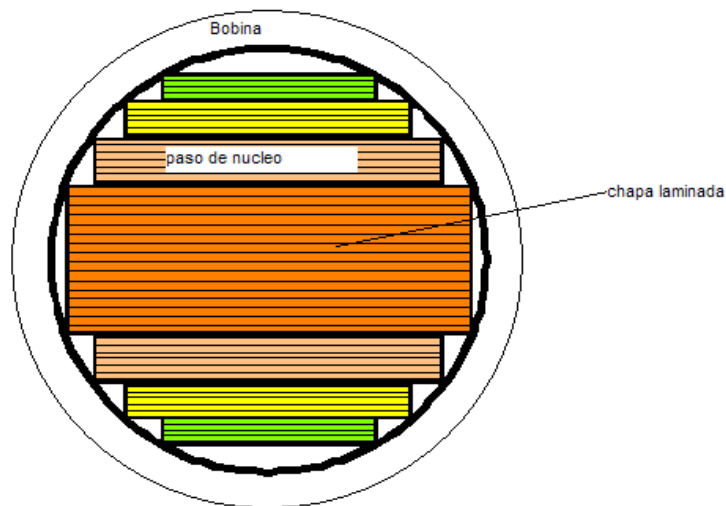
Vista en sección transversal de un núcleo laminado y el arrollamiento.
